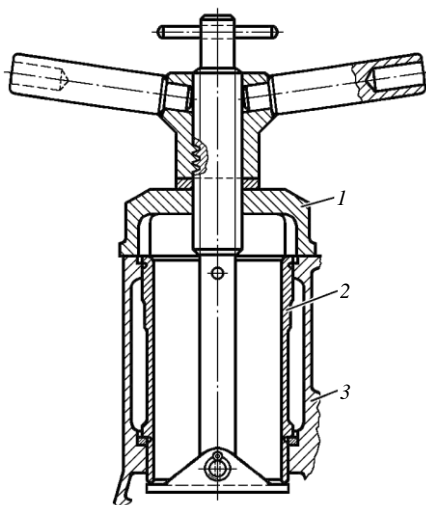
Съемник для выпрессовки гильзы из блока цилиндров:
